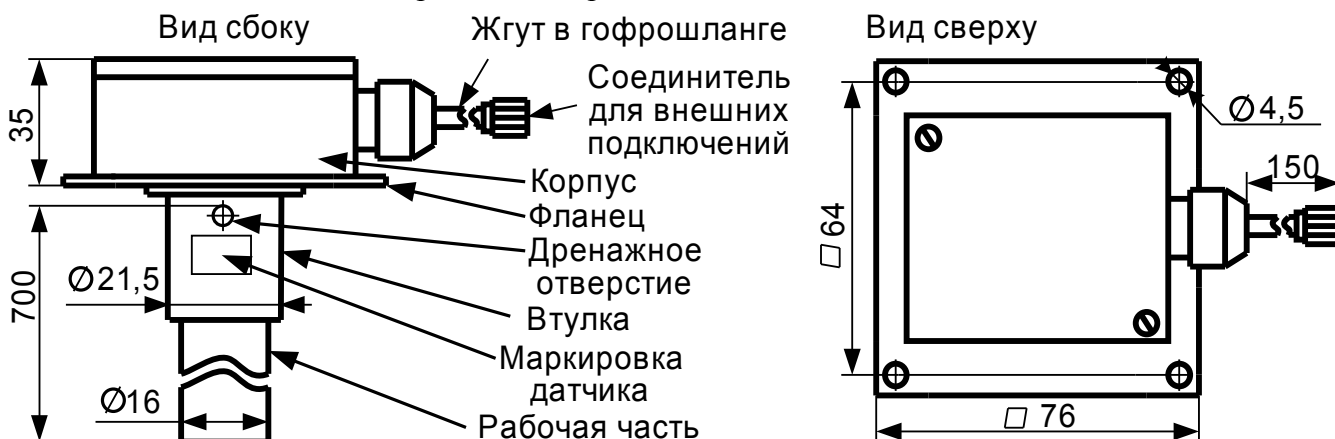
Габаритные и крепежные размеры датчика ДУ-02S базового исполнения
